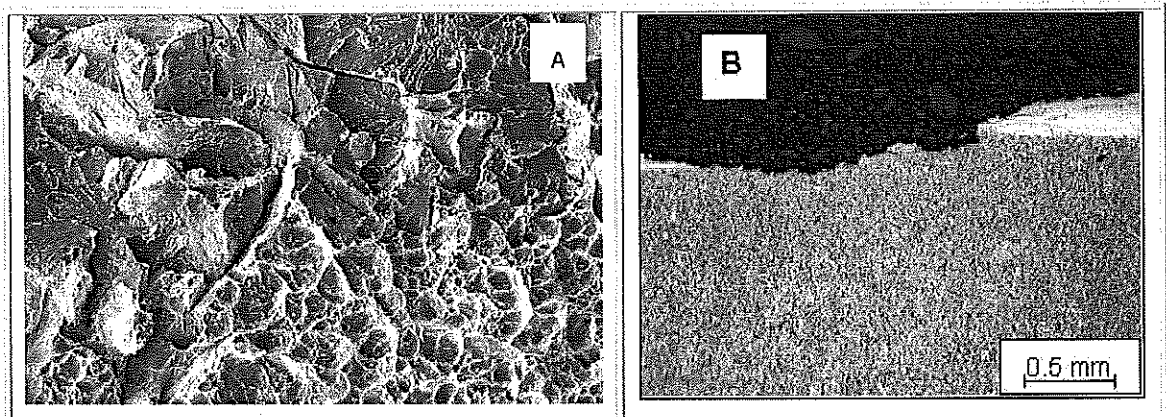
Muestra que durante la propagación de la fractura algunas secciones de esta se dieron a través de la línea de fusión (B). De esta forma se aprecia una combinación de mecanismos de fractura dúctil para el metal de soldadura austenítico y frágil para la ZAT en la línea de fusión (A).
